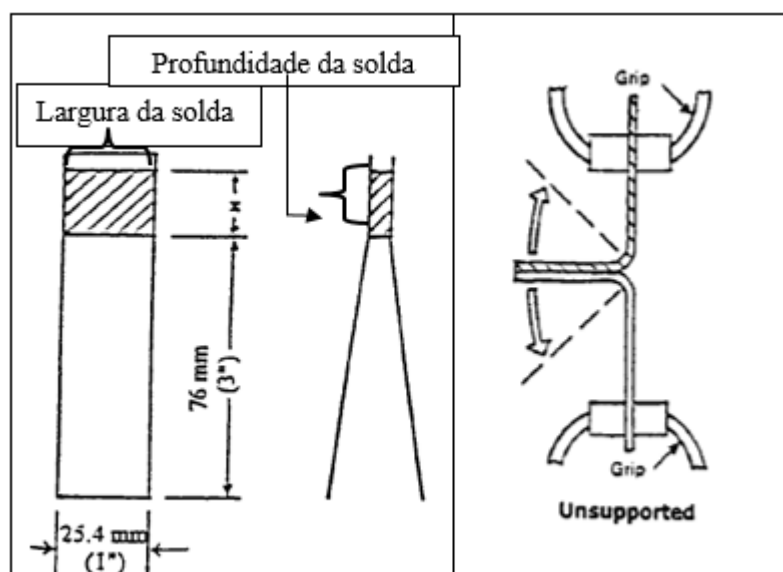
Esquerda - Tipo de provete e solda testada; Direita - Posicionamento do provete na máquina de tração. [26]
